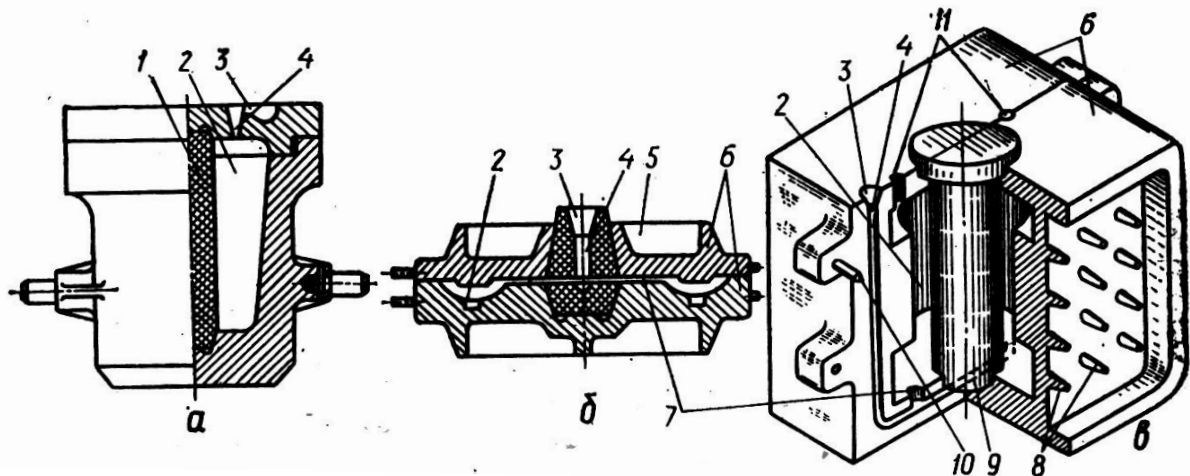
Металеві ливарні форми (кокілі):
